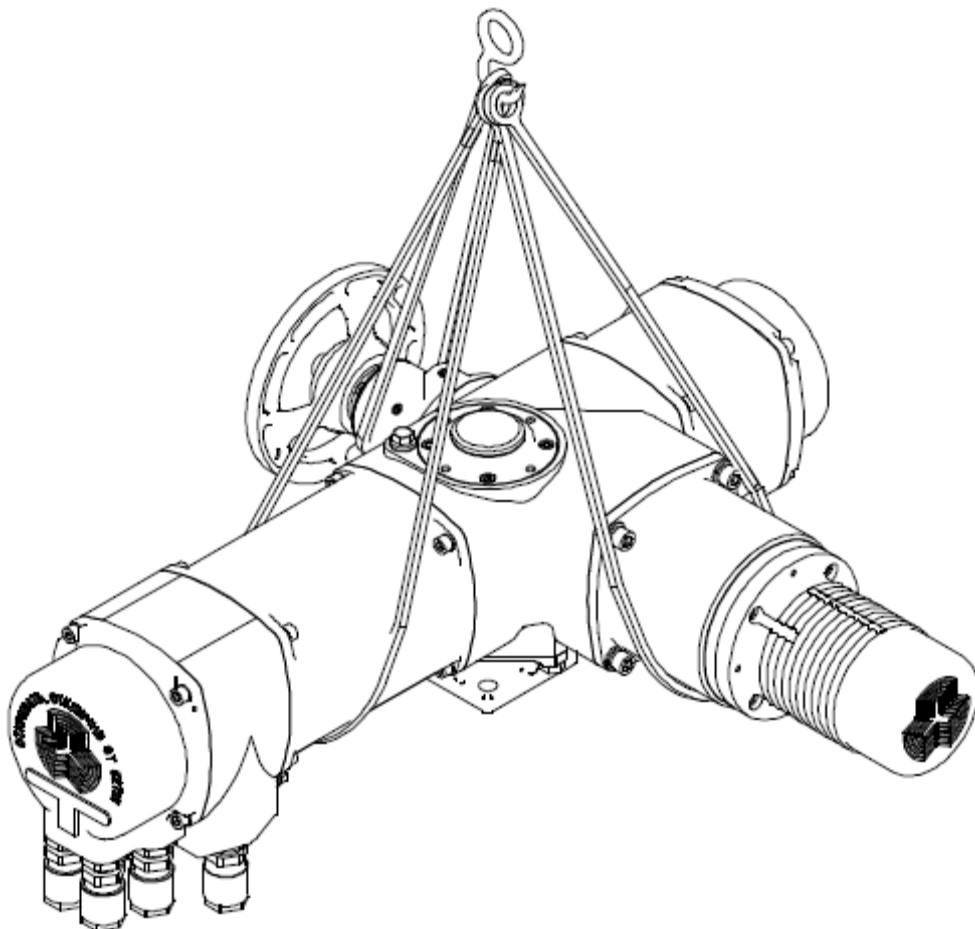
б – Схема строповки привода конструктивной схемы 41
